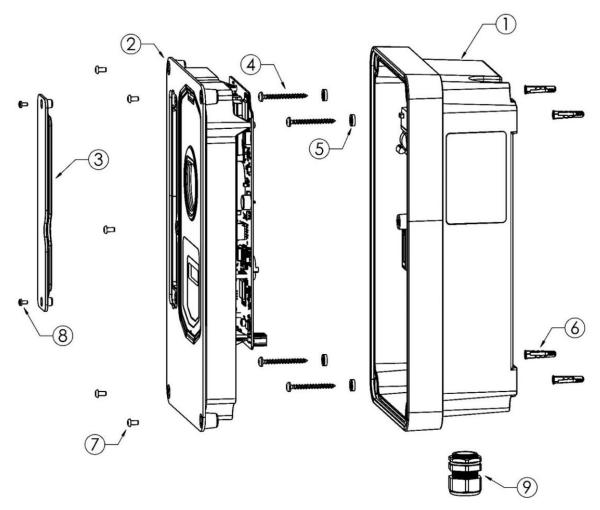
Desmontaje de componentes incluidos en el embalaje
